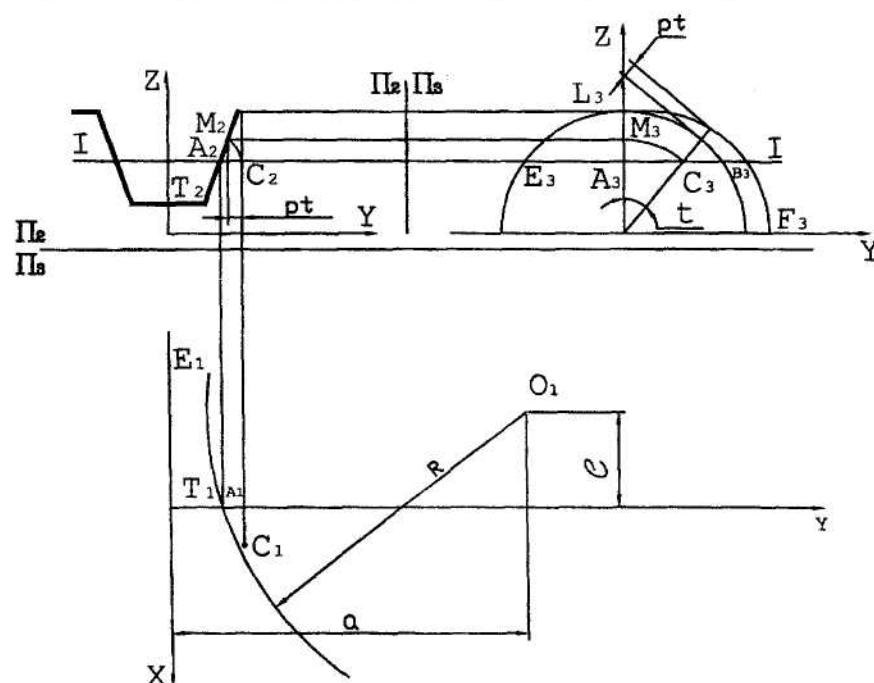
Графічне визначення вихідної інструментальної поверхні при обробці гвинтової поверхні деталі
